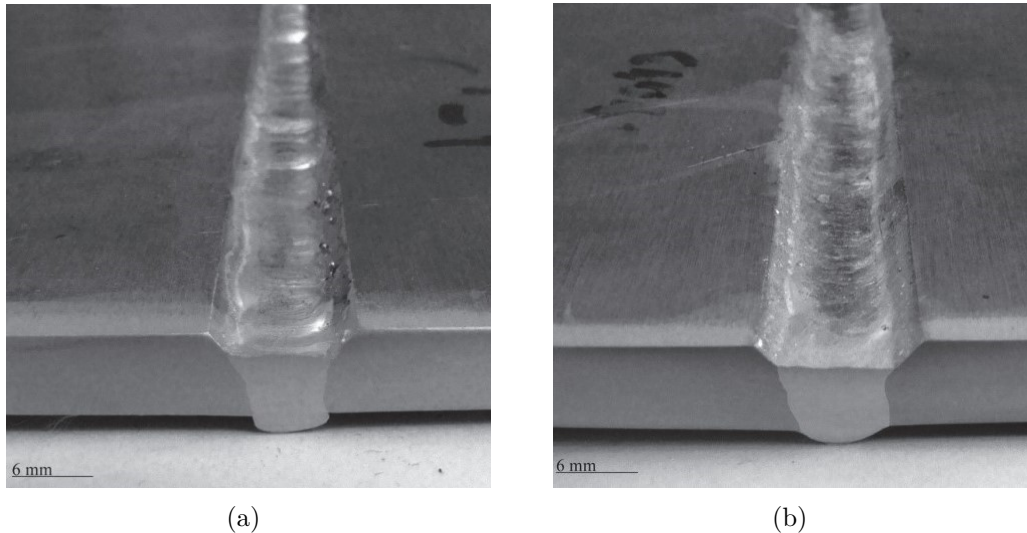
Comparação entre solda feito pelo processo MIG convencional e MIG CMT. a) Soldagem manual de Alumínio 5083 com MIG convencional (DUTRA; SILVA; MARQUES, 2013). b) Soldagem manual de Alumínio 5083 com MIG CMT (DUTRA; SILVA; MARQUES, 2013).
